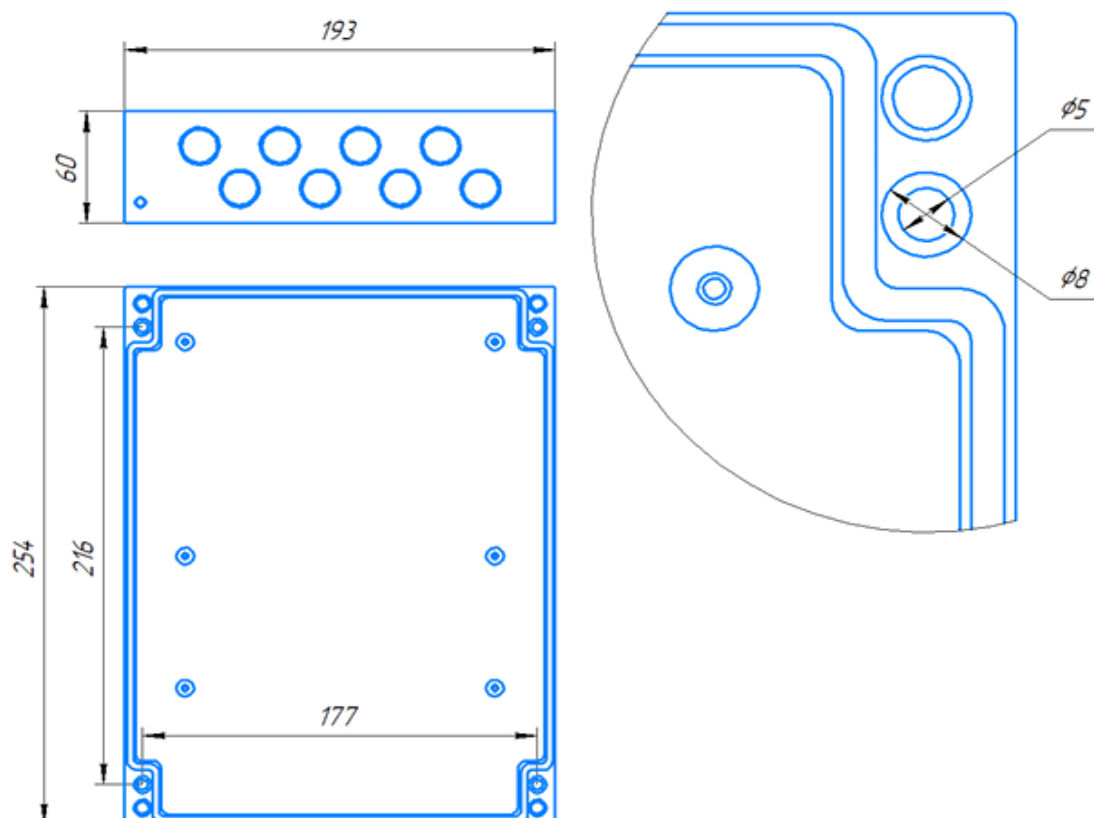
Габаритно-монтажные размеры корпуса контроллера
